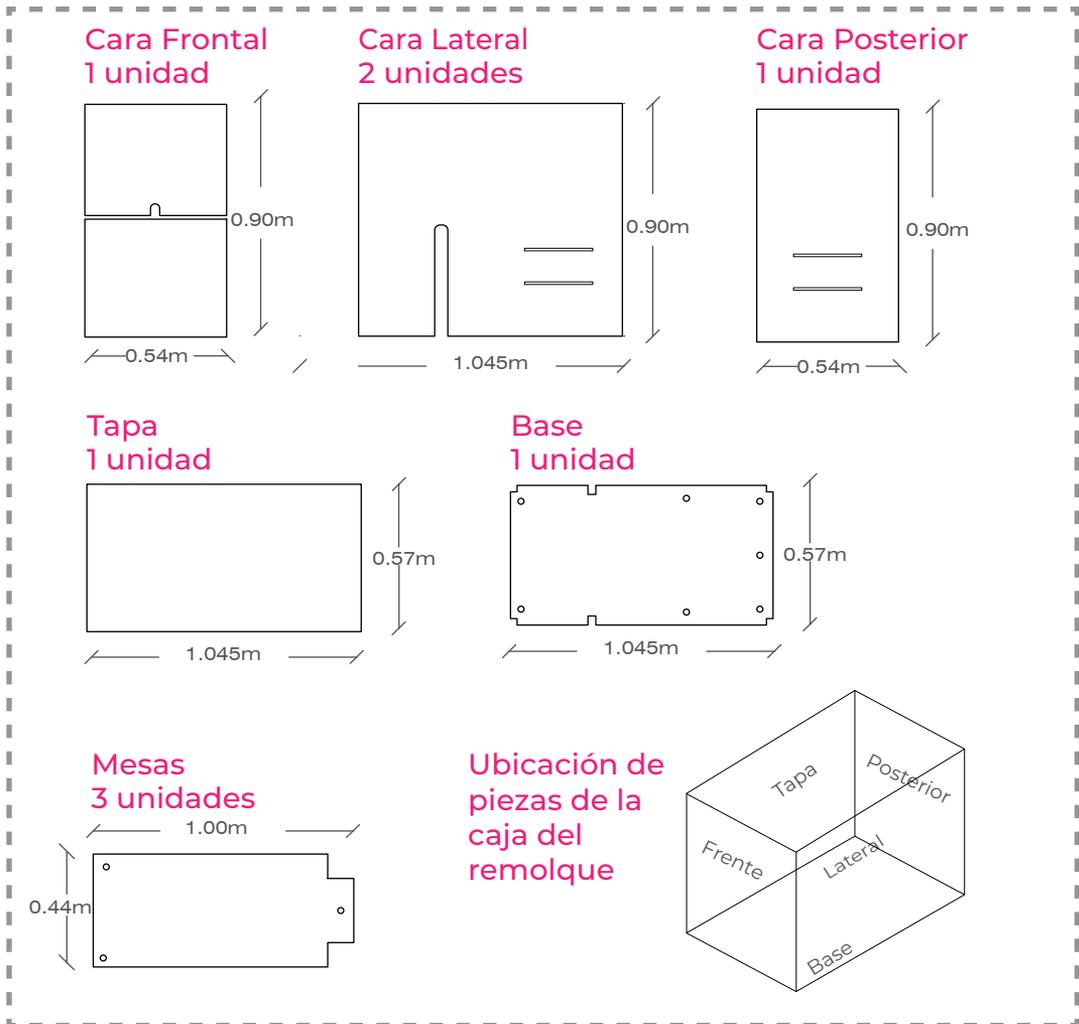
Despiece de la caja del remolque para el Aula Expandida (Fotografía propia) Morelia, Michoacán, 2022.
